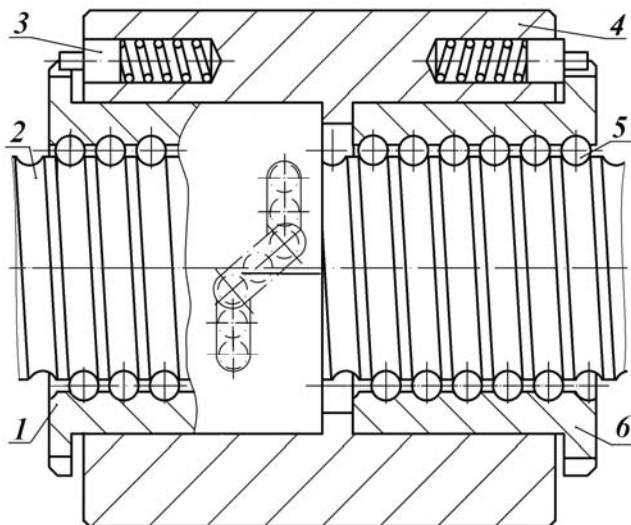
Передача винт-гайка качения с поворотом обеих гаек 4 и 6 в корпусе 4 относительно винта 1 для регулирования натяга с фиксацией их фиксаторами 3
